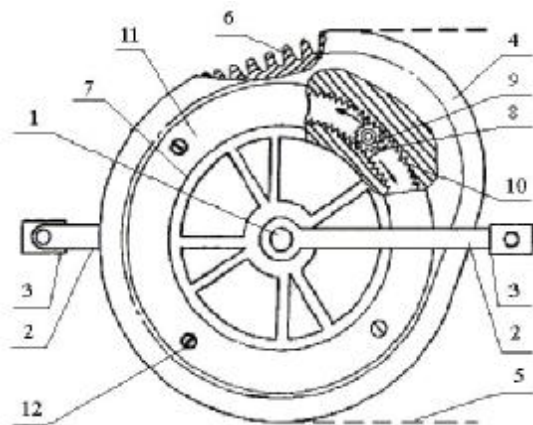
Тренажер локально направленного действия (ЛНД) – устройство для тренировки велосипедистов (УДТВ): 1 – ось; 2 – шатуны; 3 – педали; 4 – асимметричная часть; 5 – цепь; 6 – звездочка; 7 – шестерня; 8 – промежуточные шестерни; 9 – втулка; 10 – направляющее кольцо; 11 – направляющее кольцо; 12 – болт.
